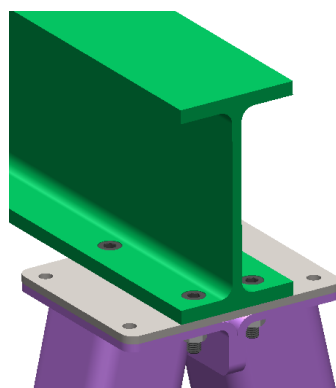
Vista de montaje de pieza N°4 en la parte superior de la estructura (Fuente 90)
